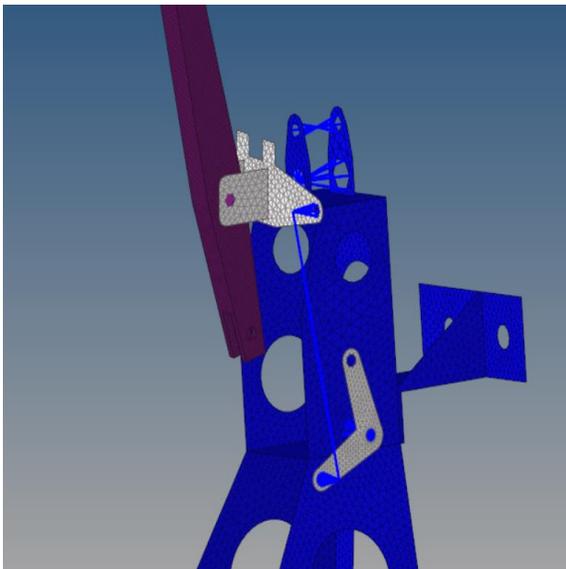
Palanca selectora de aluminio con placas de 6 mm.
